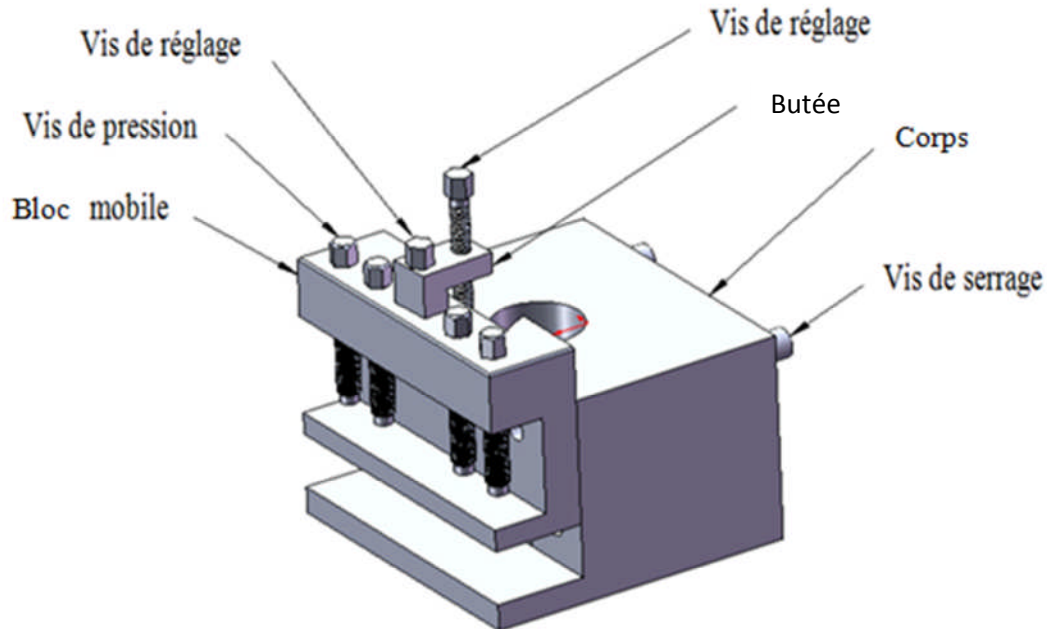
Caractéristiques dimensionnelle du porte-outil réglable
